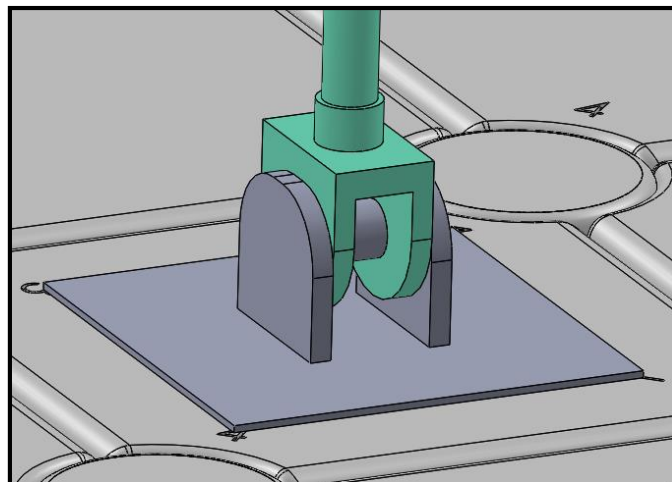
primer Apoyo, articulado, situado en la base del soporte estructural
